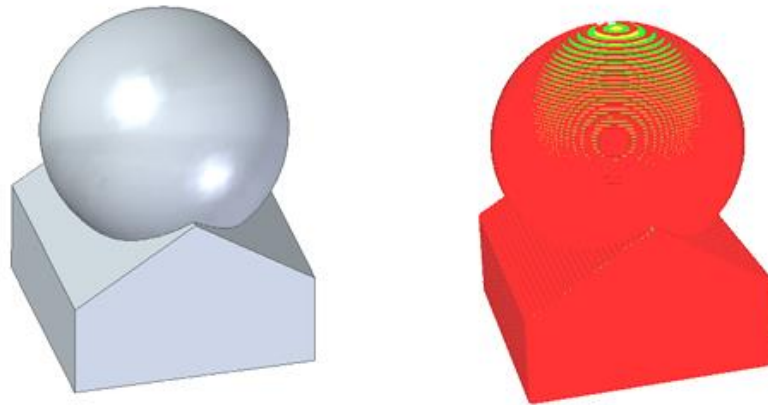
Pieza CAD y pieza preparada para fabricación aditiva (FA)
